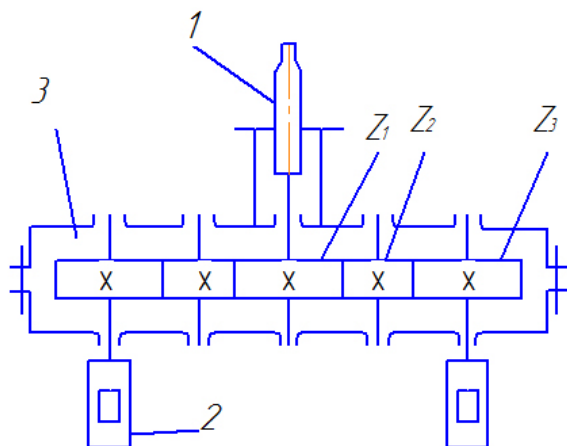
Сверлильная головка с постоянным расположением шпинделя
